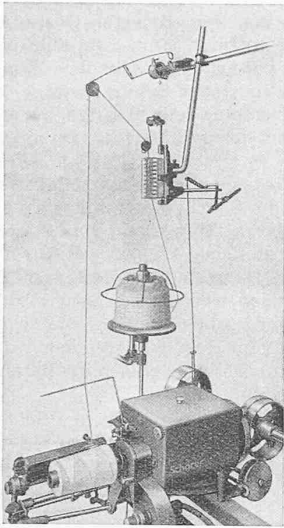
Präzisions-Kreuzspulmaschine mit einspindligem Getriebekasten
